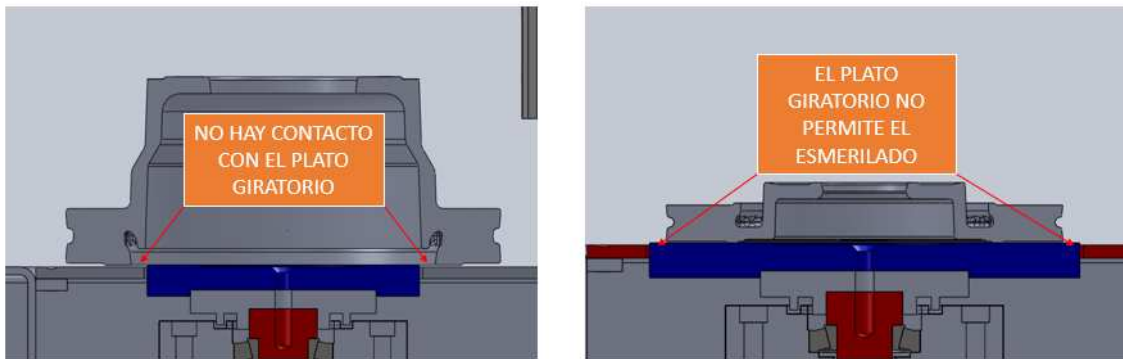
Izquierda tambor y plato pequeño, derecha disco y plato grande
